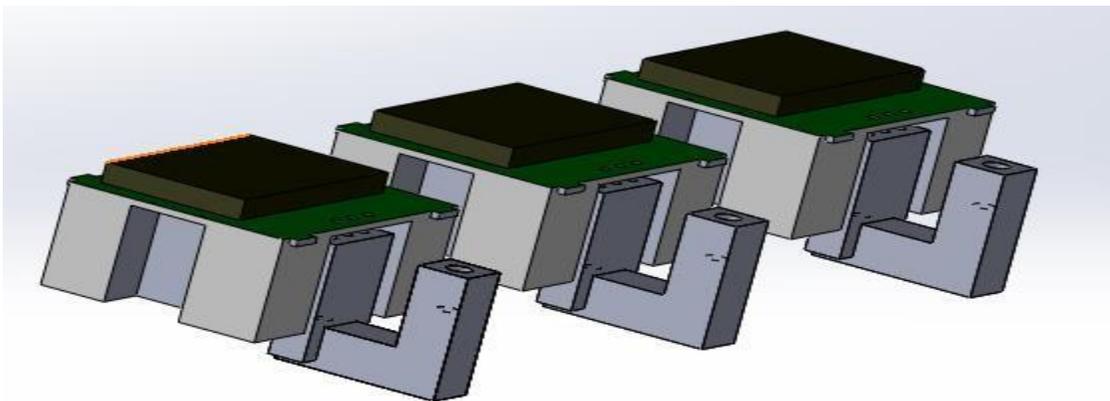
Ensamble de pieza Holding y pieza en L. (Material Aluminio 6061).
